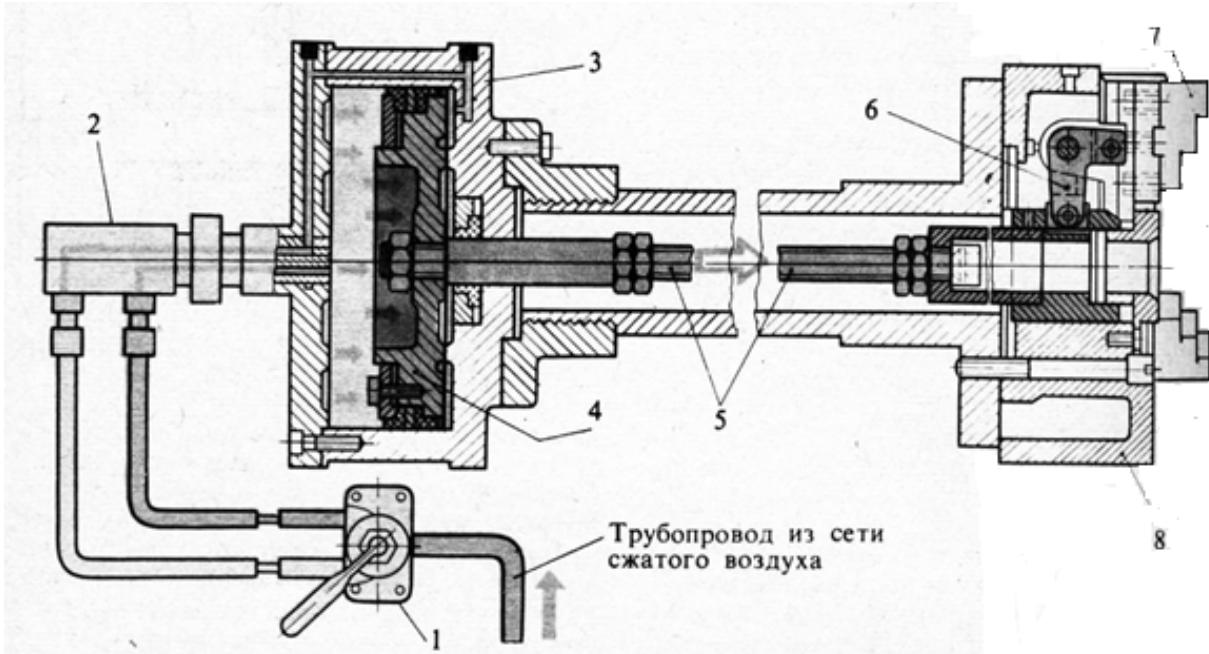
Схема пневматического привода токарного кулачкового патрона:
